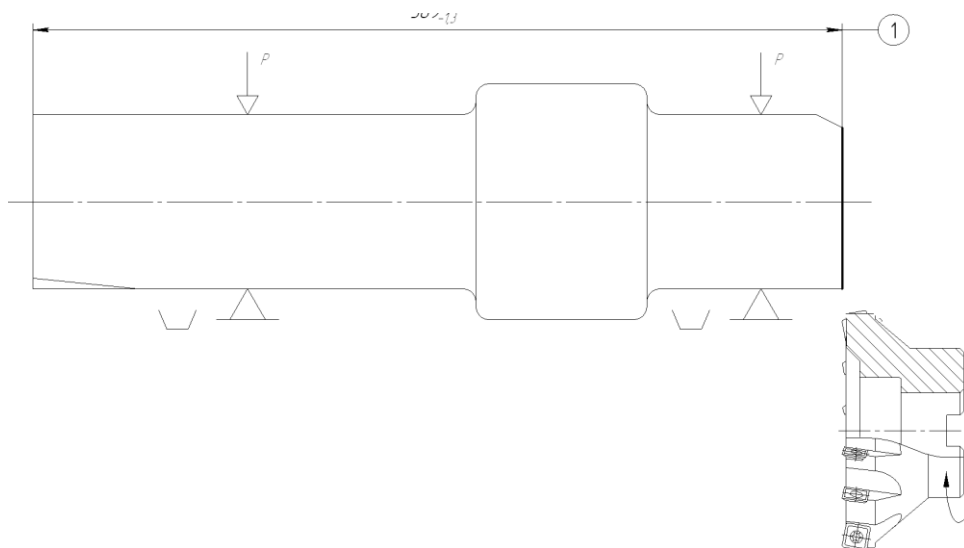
Підрізка торця на центрувально – фрезерному верстаті
